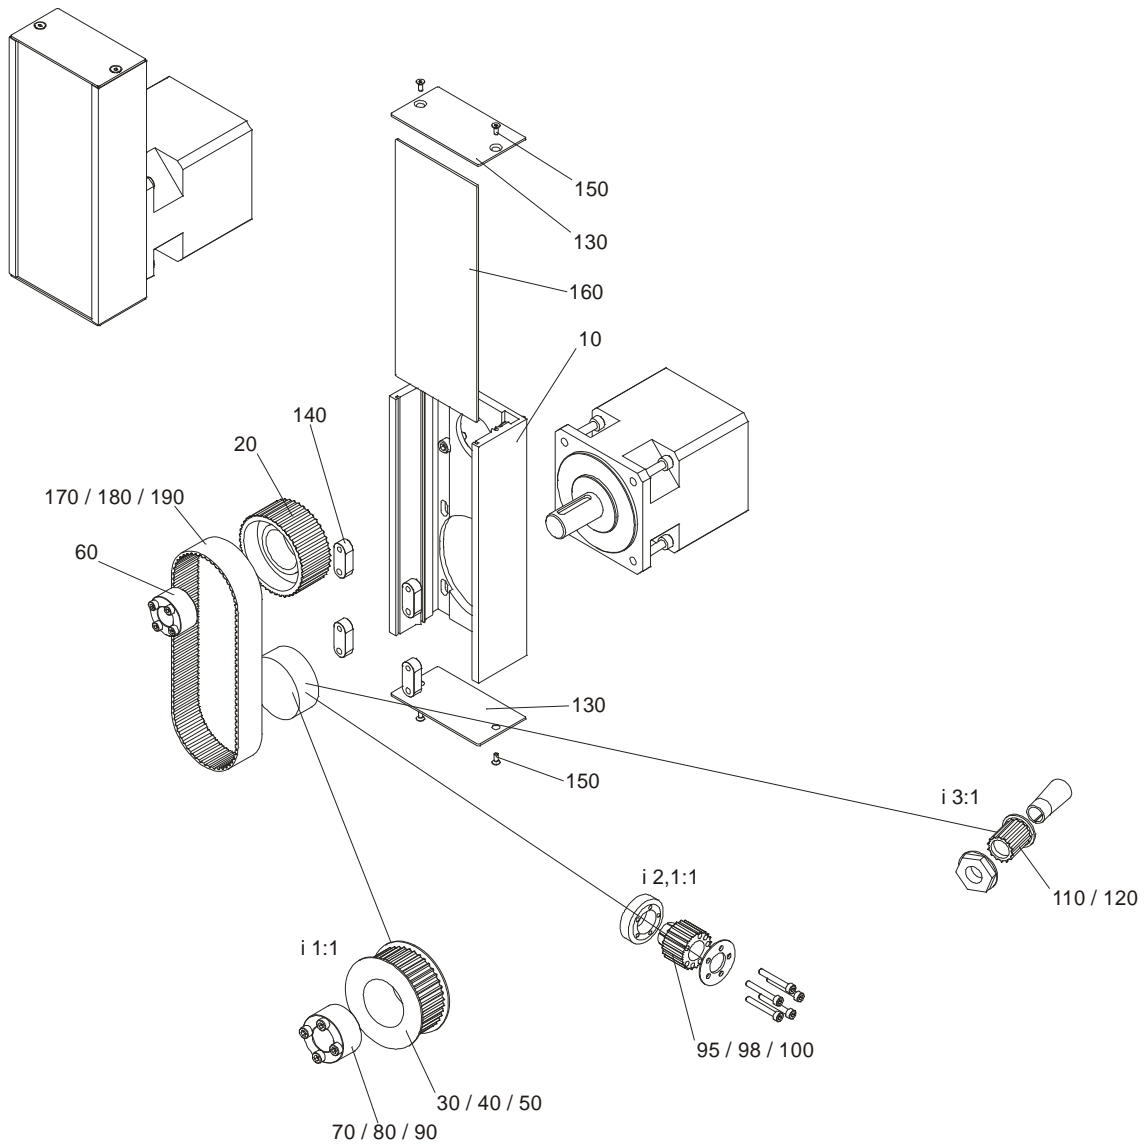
Riemengetriebe Modul 160/15C, Explosionszeichnung
